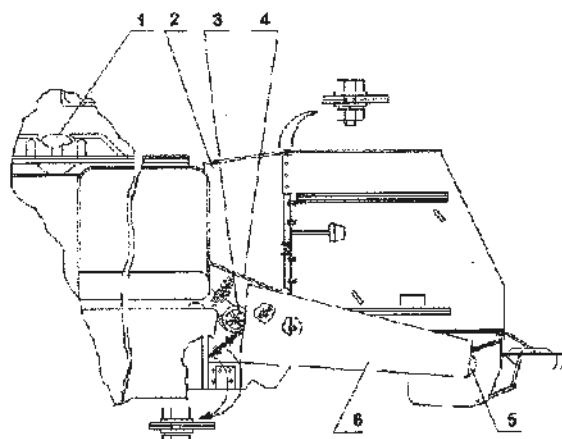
Измельчитель-разбрасыватель (вид слева):
